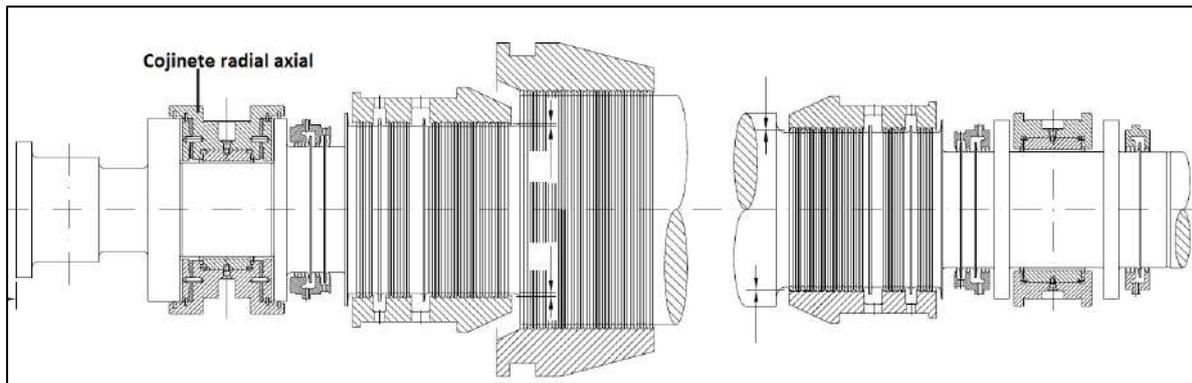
Vista general del rotor de la turbina donde se especifica la posición del cojinete radial-axial.
